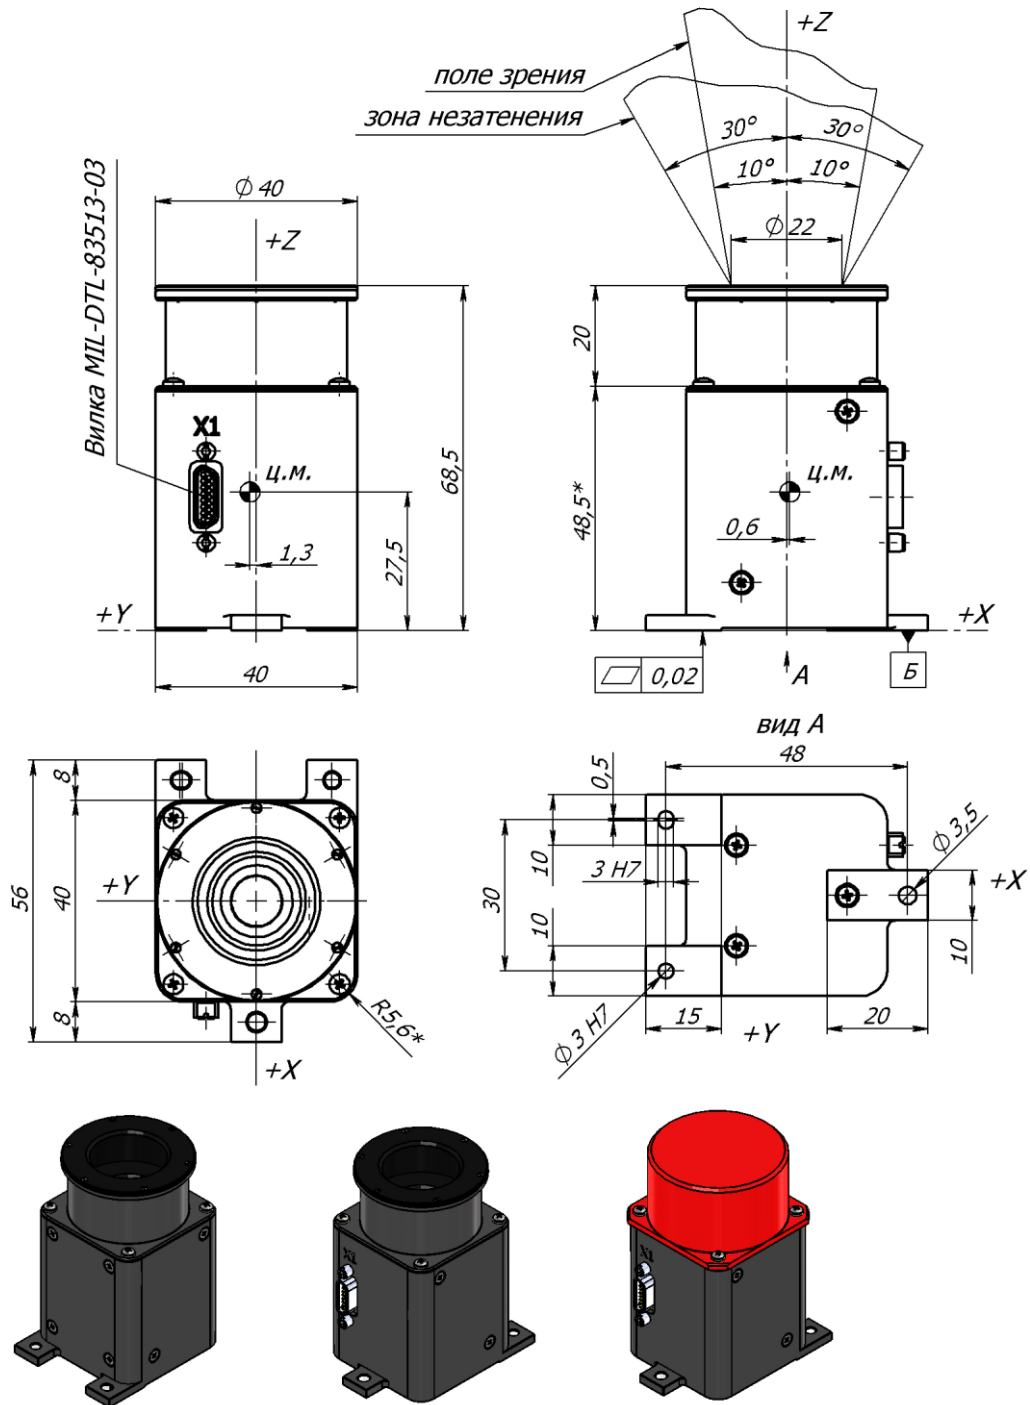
Габаритный чертеж датчика АЗДК-1
